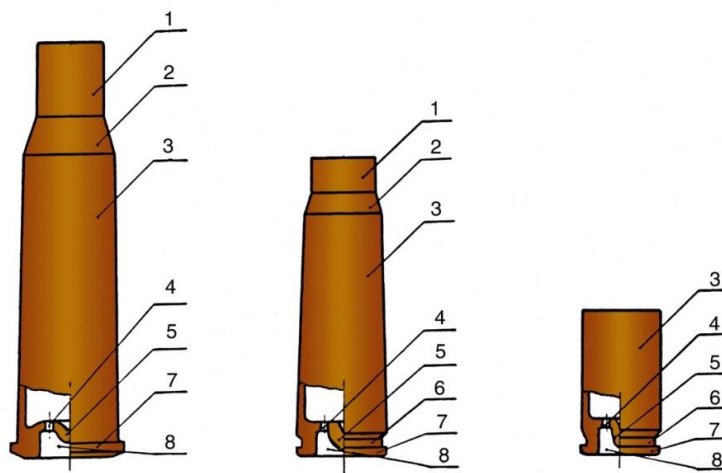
Образцы конструкций гильз: 1 – дульце; 2 – скат; 3 – корпус; 4 – запальное отверстие; 5 – наковальня; 6 – проточка; 7 – фланец; 8 – капсюльное гнездо
